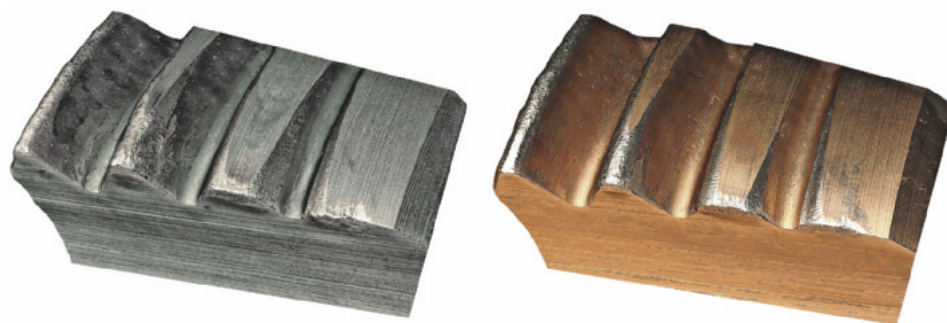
Gewindeschneiden in EN-GJS-600-3 (GGG60) mit einem M16x1,5 Grundlochgewindebohrer. Bei einer Schnittgeschwindigkeit von 30 m/min und einer Gewindetiefe von 1,5xD ist das TiCN-beschichtete Werkzeug (links) stark verschlissen und weist
